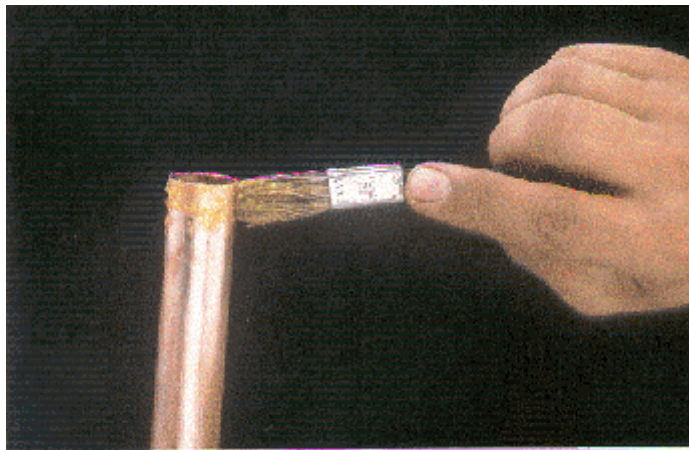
Aplicação de pasta de solda(fluxo) na ponta do tubo e na bolsa da conexão, de modo que a parte a ser soldada fique completamente coberta pela pasta.
